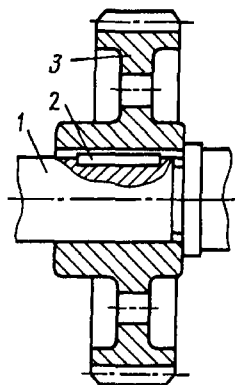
Сборочная единица (зубчатое колесо):
